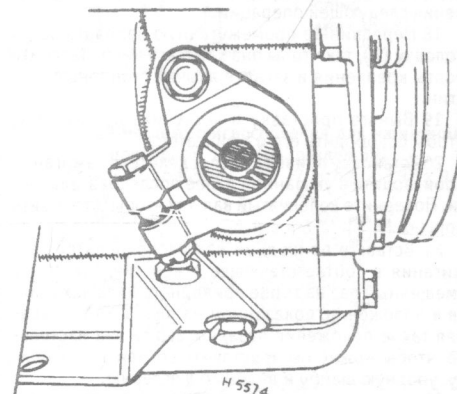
А Схема установки приводного вала распределителя зажигания (см. раздел 45)
